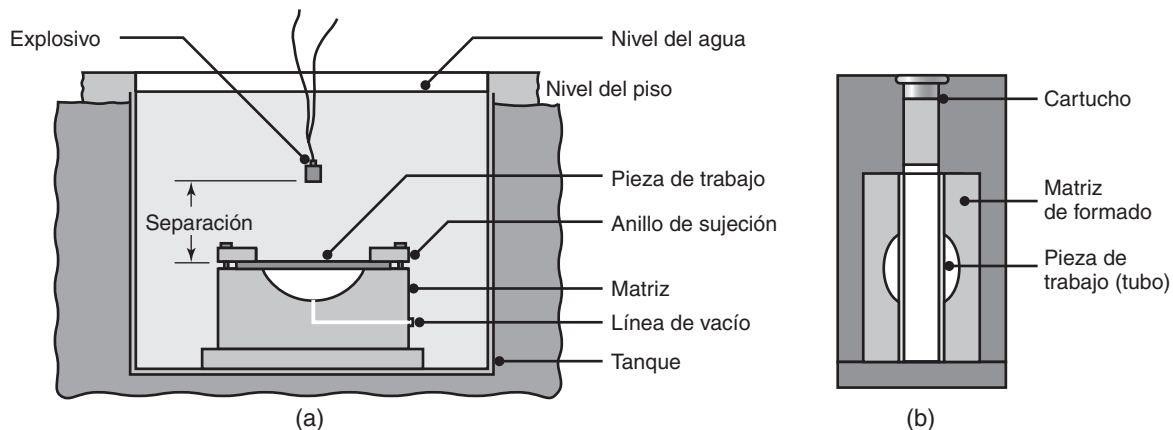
(a) Esquema del proceso de formado por explosión. (b) Ilustración del método confinado de abombado de tubos por explosión.
